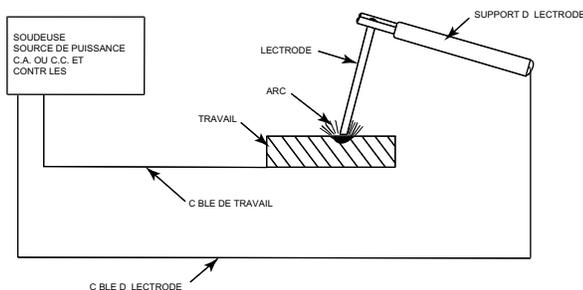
Circuit de soudage pour soudage à l'arc à métal couvert (Baguette).
